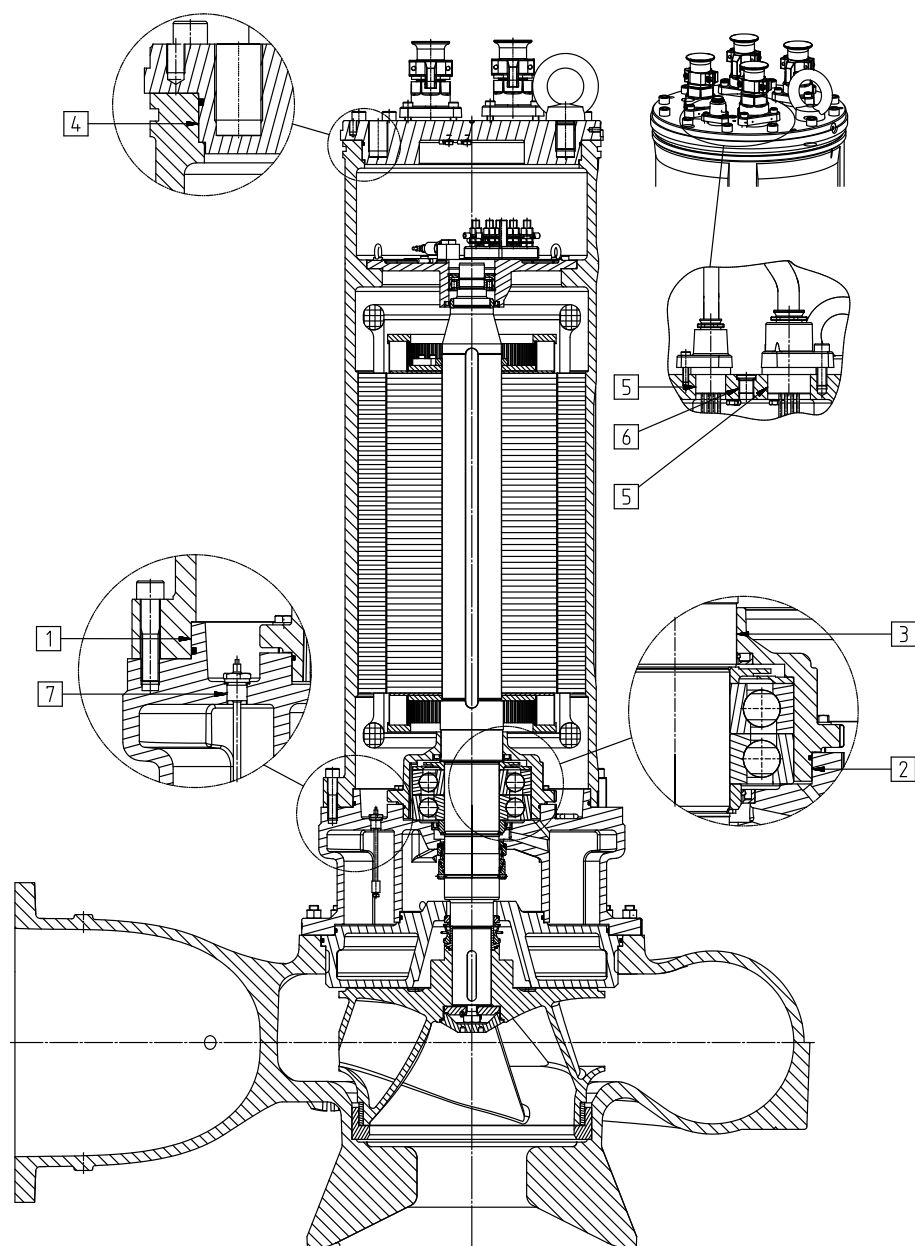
Ex-Spaltflächen bei explosionsgeschützten Motoren
